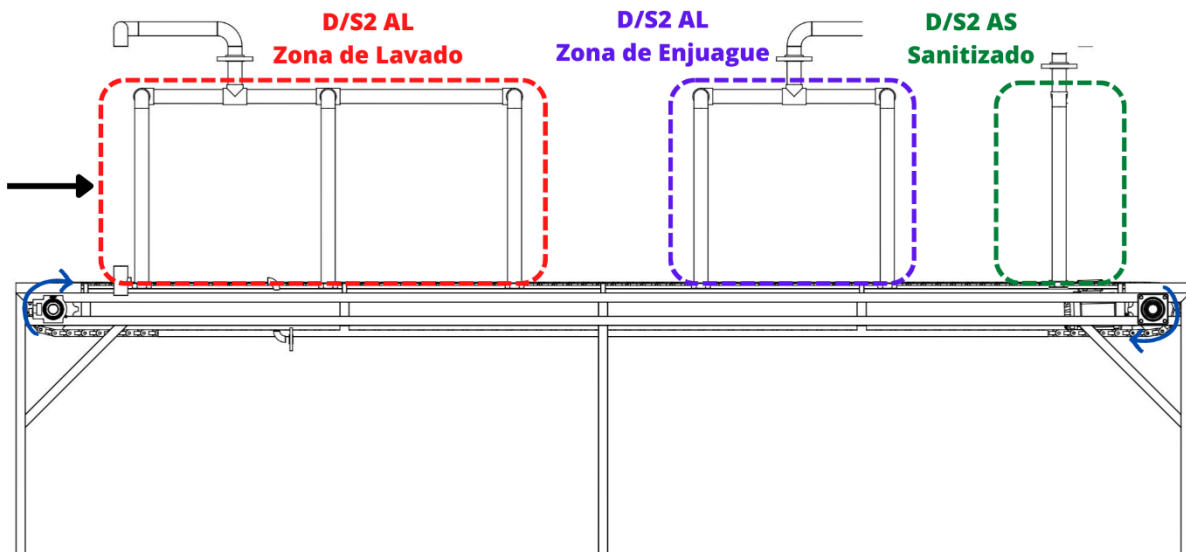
Etapas de Lavado. Fuente: Propia
